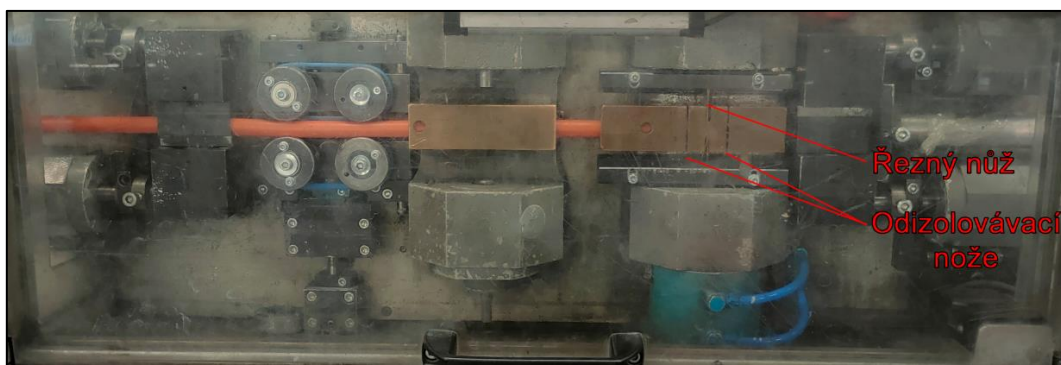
Mechanismus pro navíjení a podávání kabelu.
